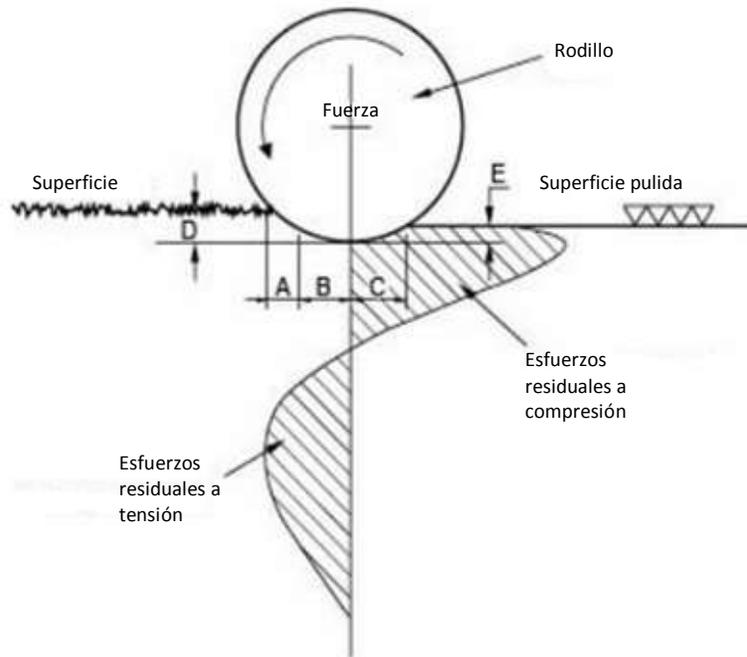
Proceso de bruñido con rodillo duro. Fuente: "Tool life enhancement in cold forging by locally optimized surfaces", K. Wagner, R. Völkl, U. Engel, University of Erlangen-Nürnberg.
